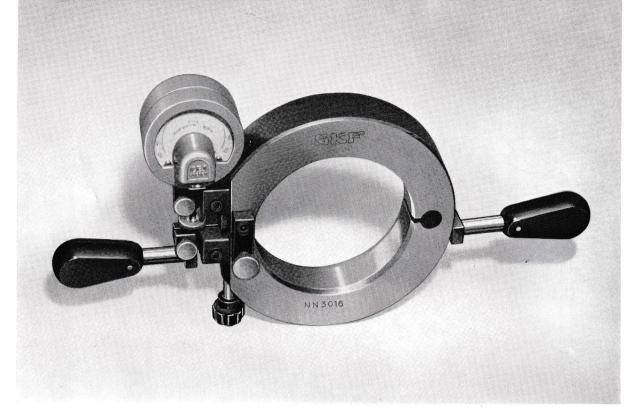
Herramienta de medir para rodamientos de rodillos cilíndricos
